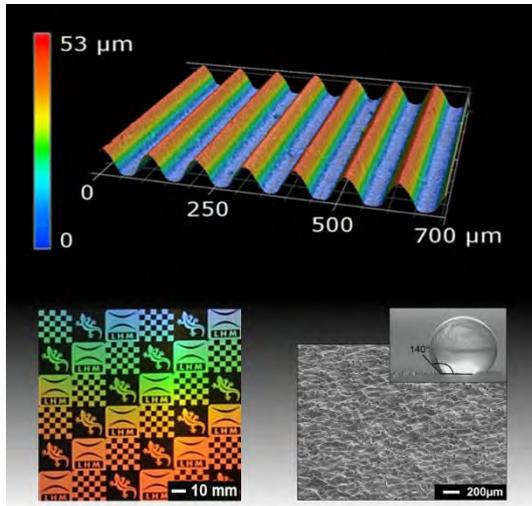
Beispiele für mit Hochrate-Lasermikrobearbeitung prozessierte Oberflächen
